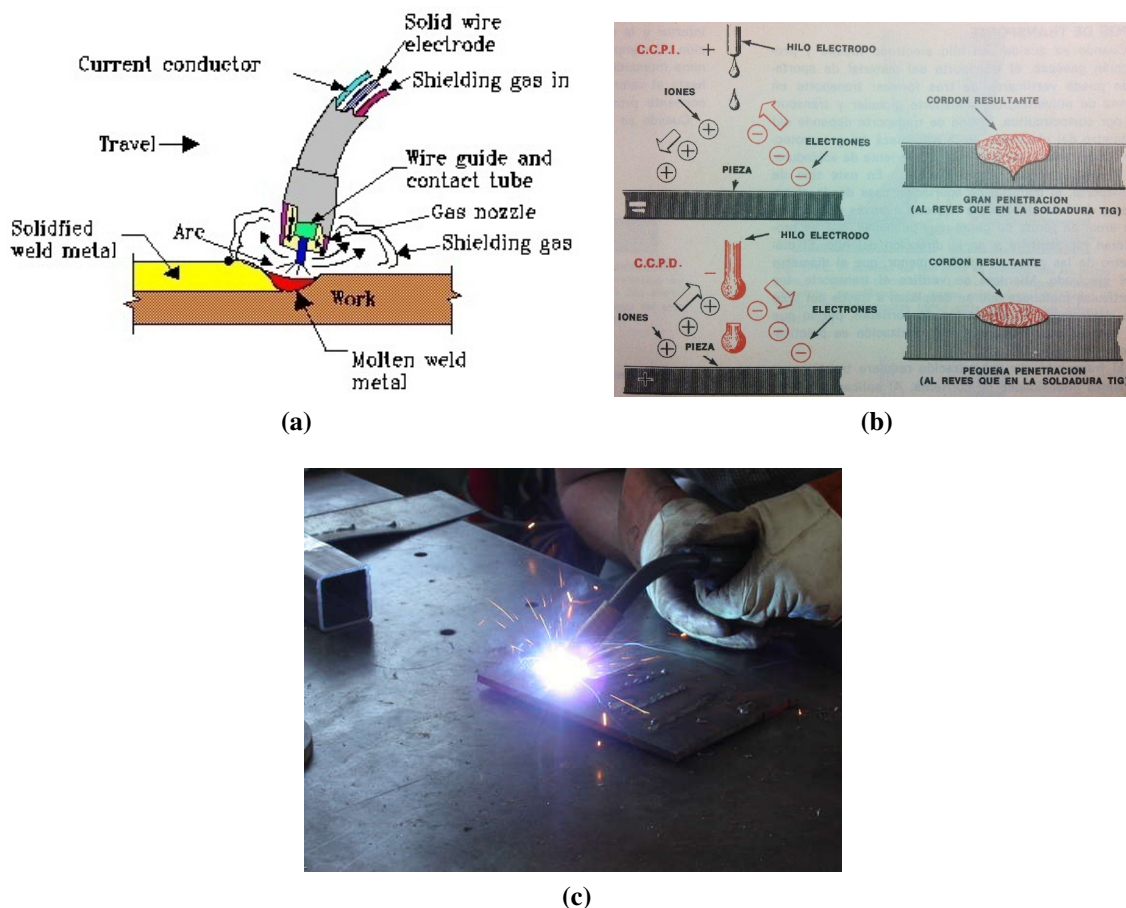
Esquemización del proceso de soldadura por arco eléctrico GMAW. a) Principio de trabajo del proceso GMAW. Fuente [7]. b) Influencia de la polaridad en la soldadura GMAW. Fuente [6]. c) Proceso GMAW real. Fuente [8].
